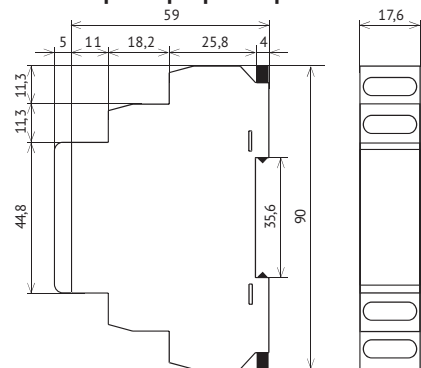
Габаритные, установочные и присоединительные размеры реле OptiRel C RT
